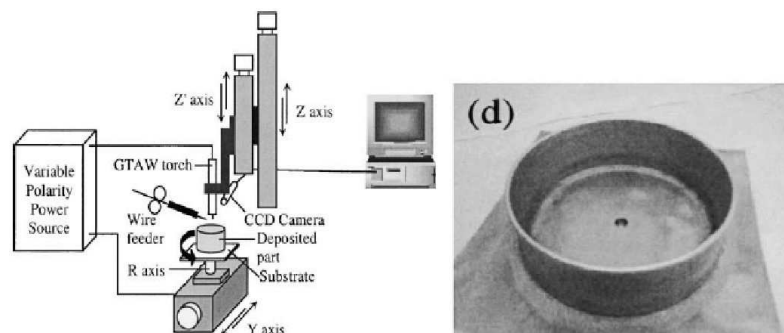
Fabrication par WAAM d'une pièce en aluminium en utilisant le procédé de soudage TIG[52]
